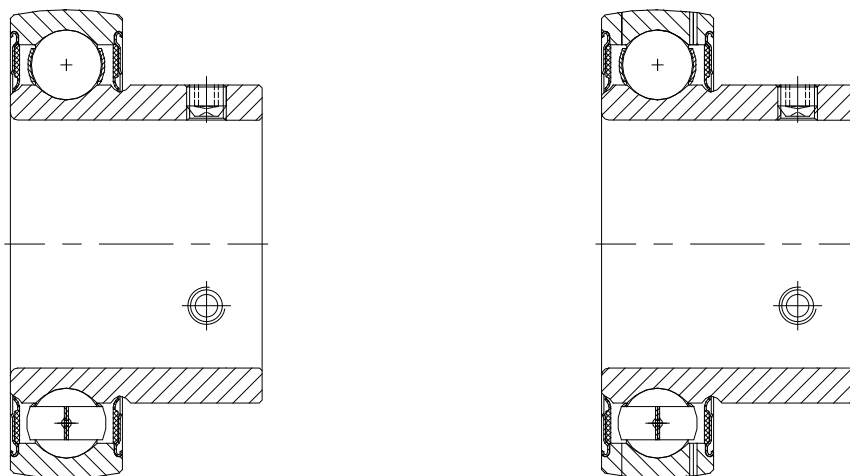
корпусные подшипники NKE конструкций AY и GAY
